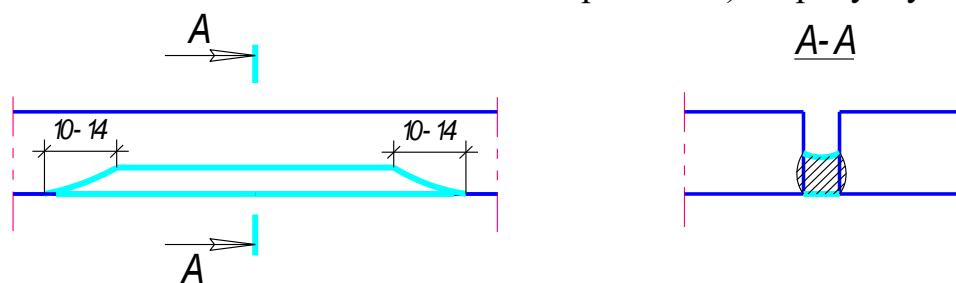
Конфигурация прихватки в сварном шве
